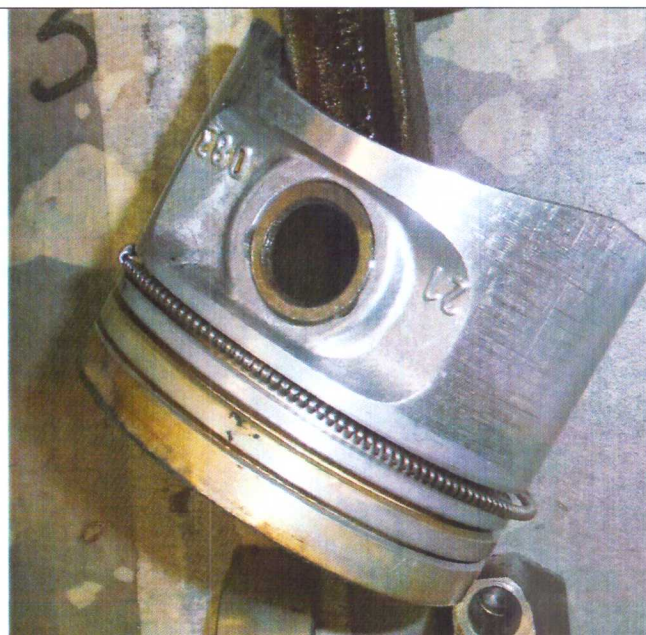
Внешний вид боковой поверхности поршня второго цилиндра по окончании длительных испытаний двигателя при работе на базовом масле Castrol EDGE
